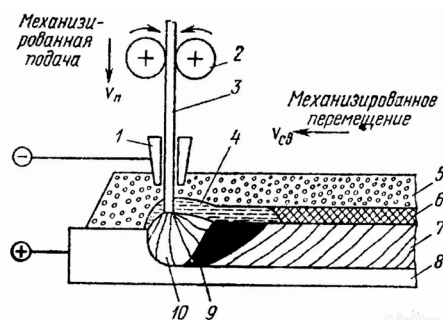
Схема автоматической сварки проволокой сплошного сечения под слоем флюса
